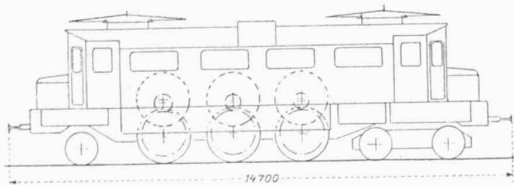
Schweizerische Bundesbahnen. — Typ 1-3A-2.
